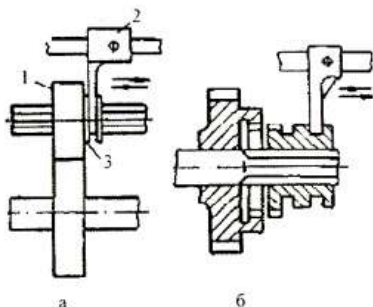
Циліндрична зубчаста передача з рівнобіжними вісями і ковзною зубцюватою кареткою: а – для включення коліс із прямими зубами та кареткою; б – для включення коліс з косими зубами
